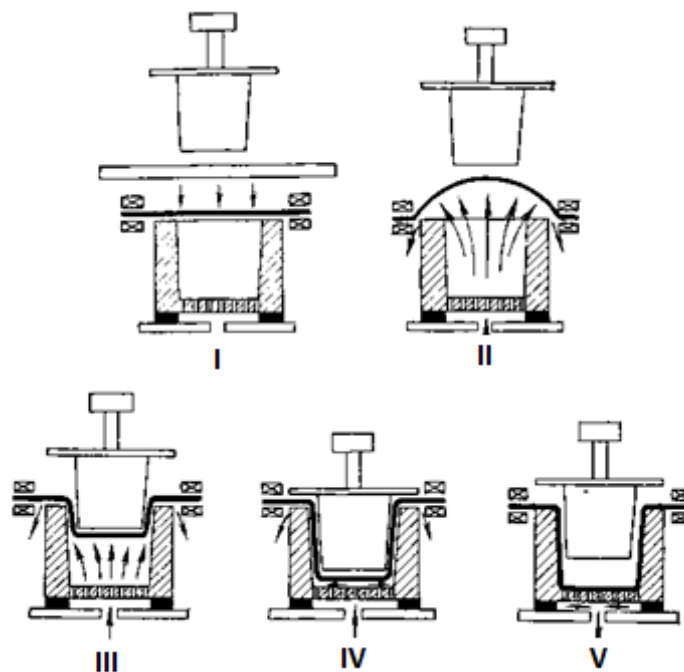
Негативне формування із пневмомеханічною витяжкою.
